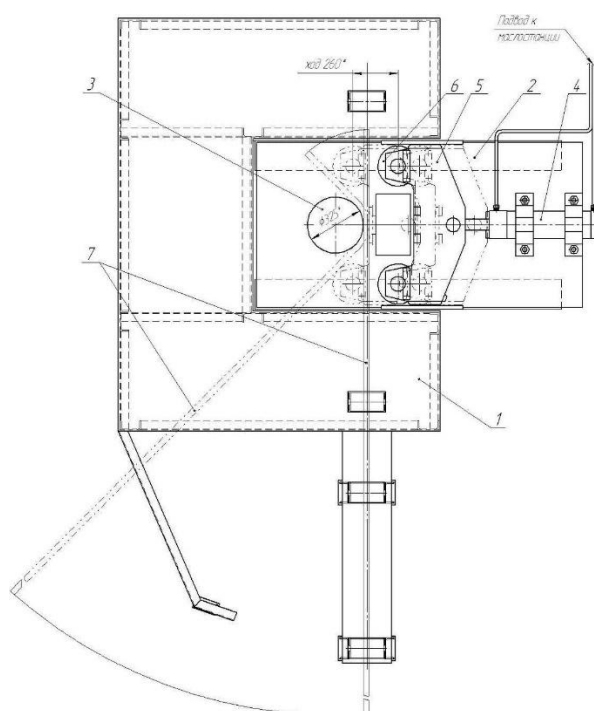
Модернізований прес для згинання бандажів виливниць
